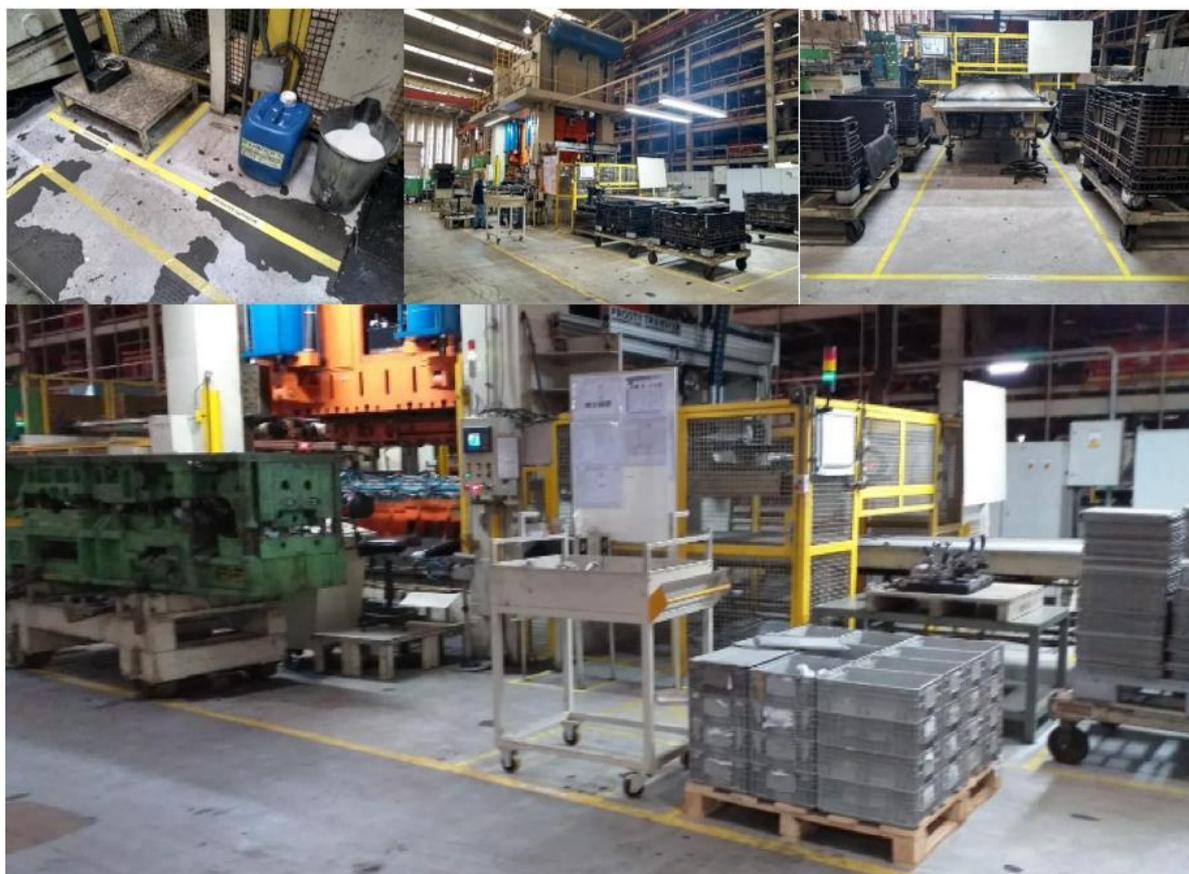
Fotos com a situação ao redor da máquina piloto anteriormente a aplicação do 5S.
